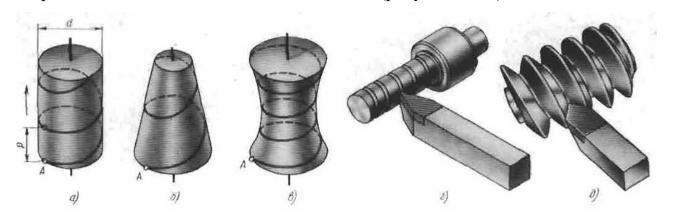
Образец нарезания резьбы на цилиндрическом стержне резцом
